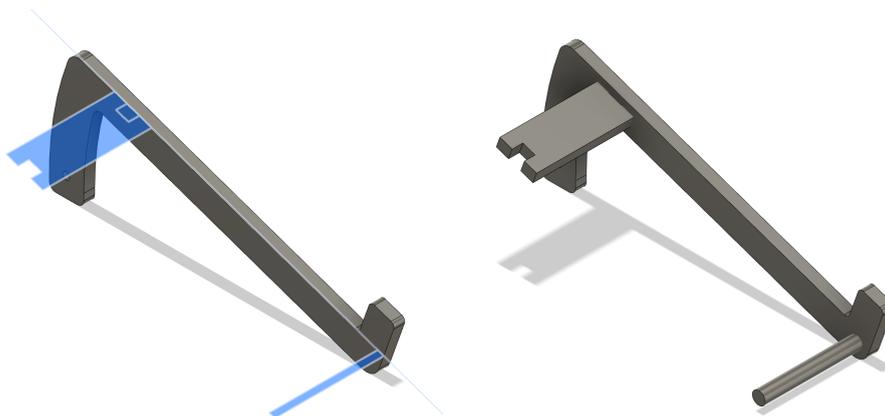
Vue du plan d'esquisse des pièces transversales mobiles)
